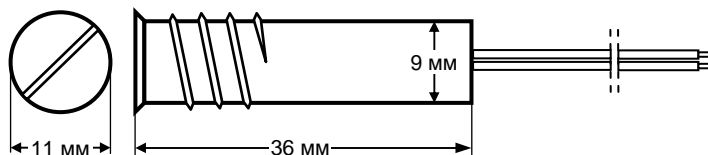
Геркон извещателя К-3 в металлическом корпусе
